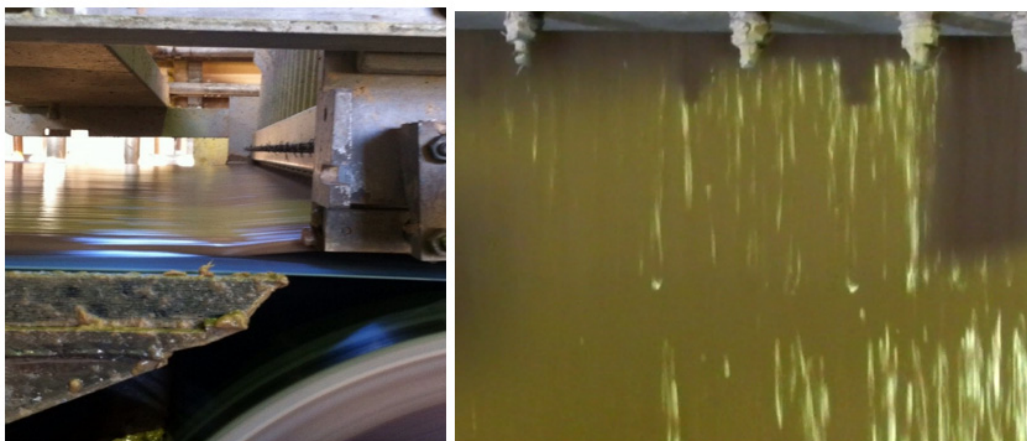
Процесс напуска массы (вид сбоку и сверху)
